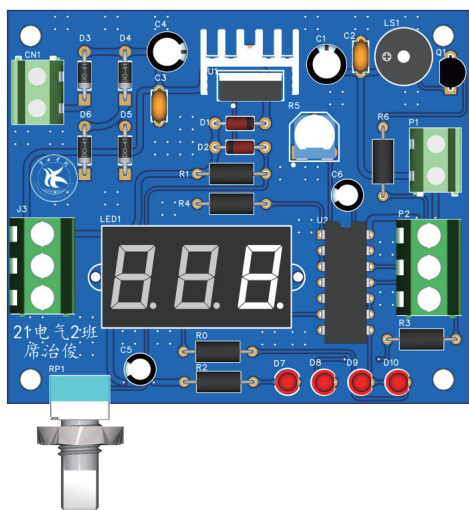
复刻项目直流可调电源 PCB 板 3D 仿真视图
